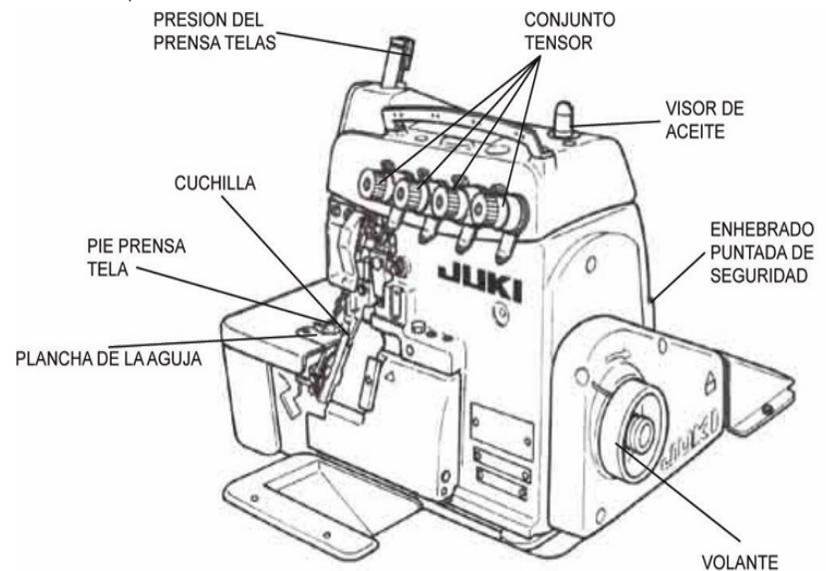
Partes de la máquina overlock industrial. Fuente: Juki M. (2002).
